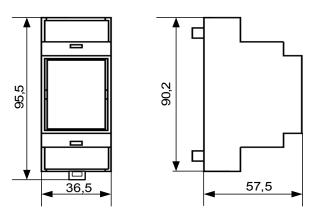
Габаритные и присоединительные размеры преобразователя
